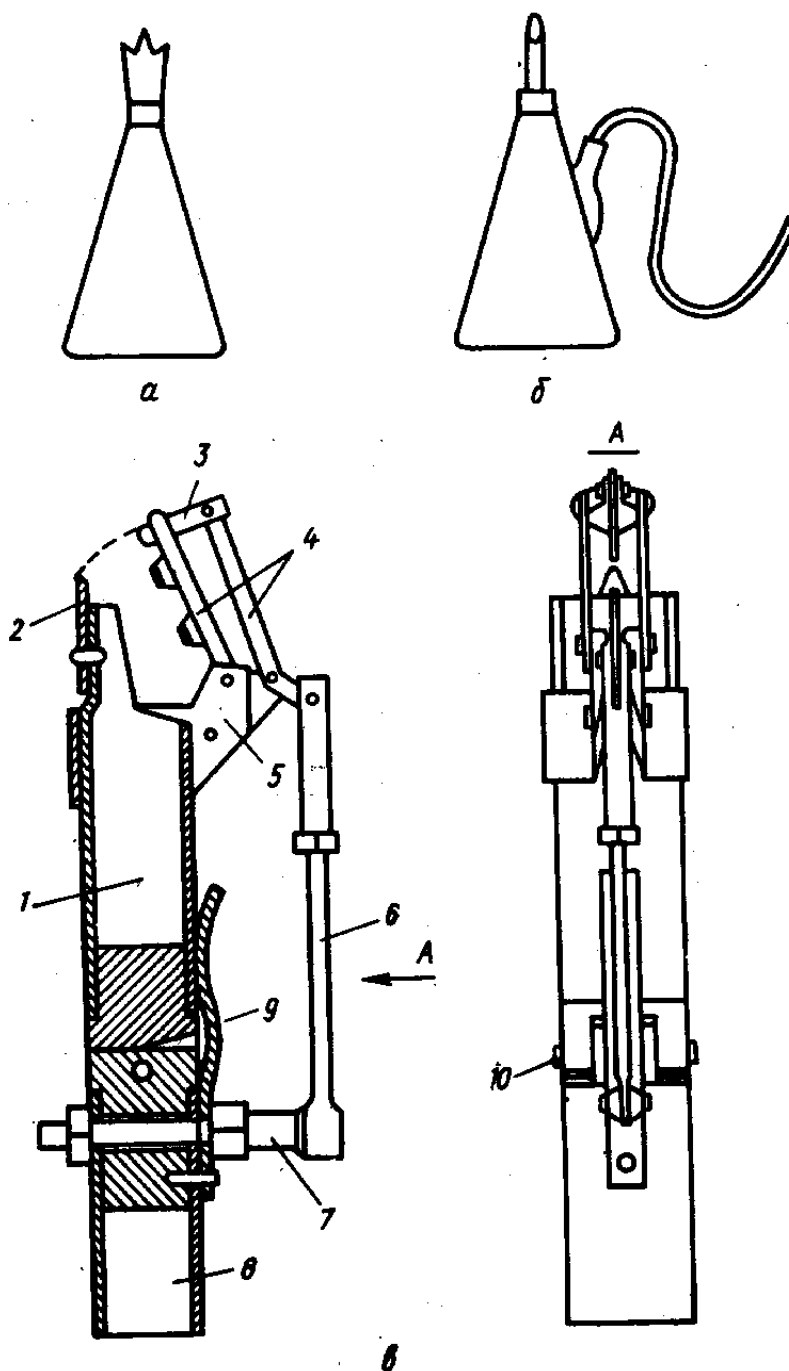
Приспособления и устройства для сбора живицы пихты:
